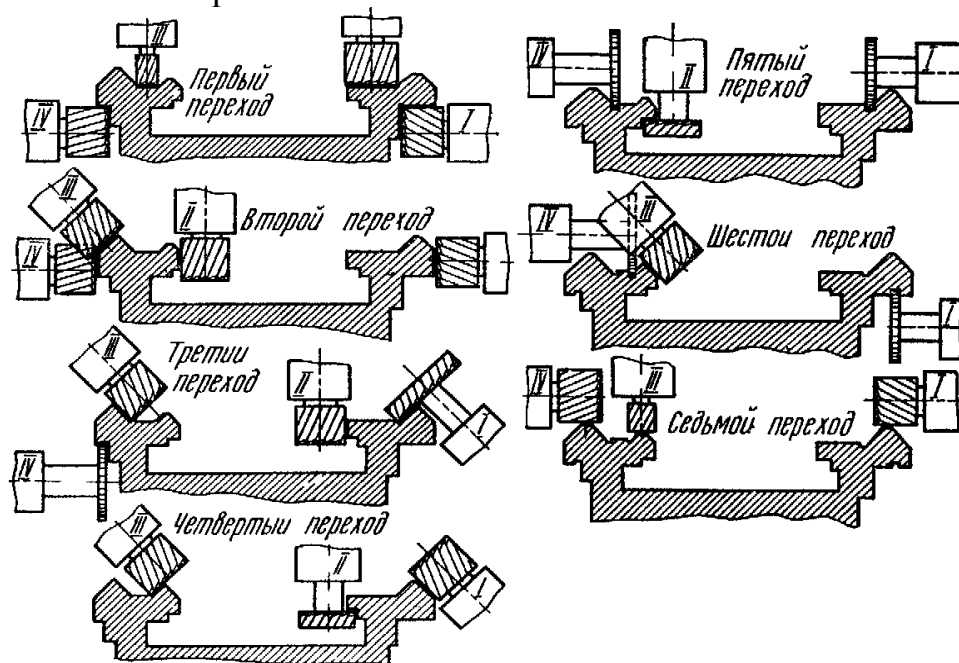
Схема фрезерования направляющих станины станка со сменой фрез
